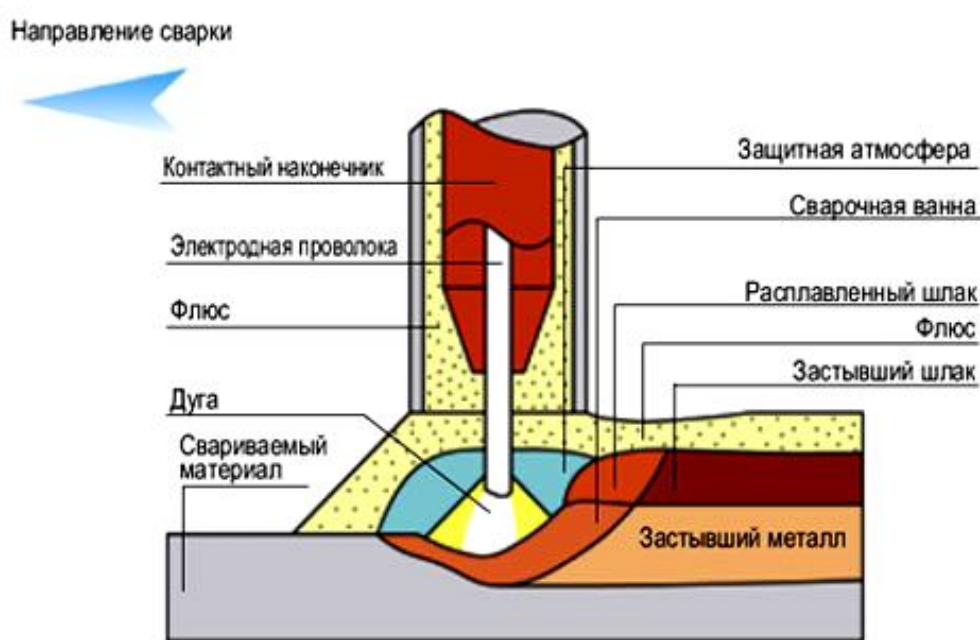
Схема автоматической сварки под слоем флюса
